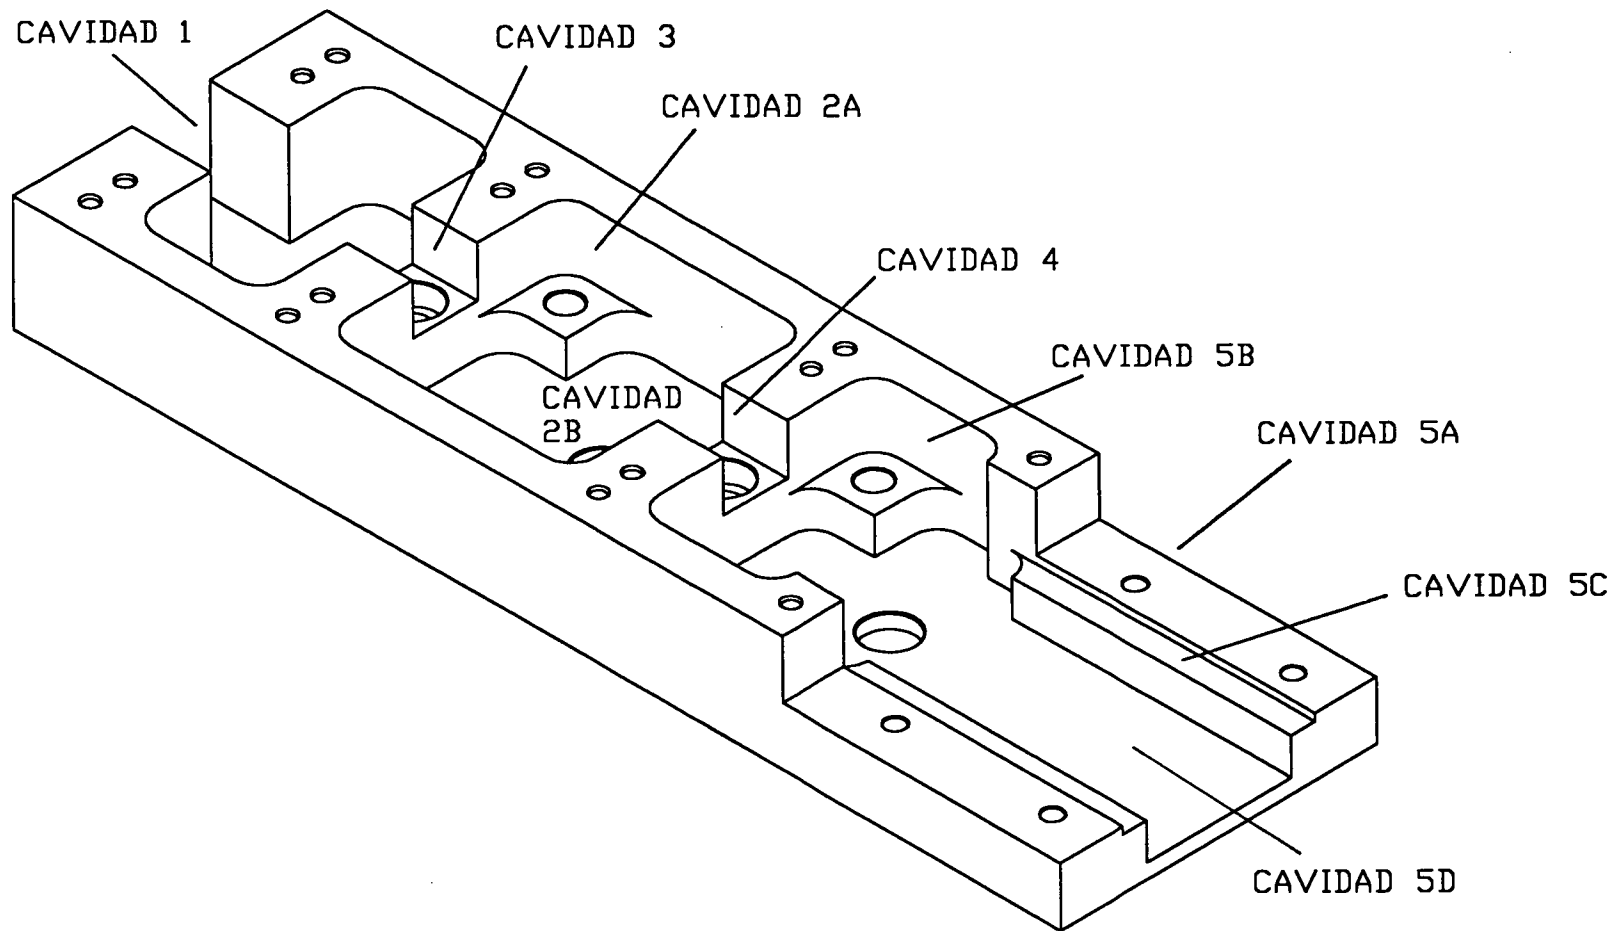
Vista axonométrica de la pieza: placa 3.
